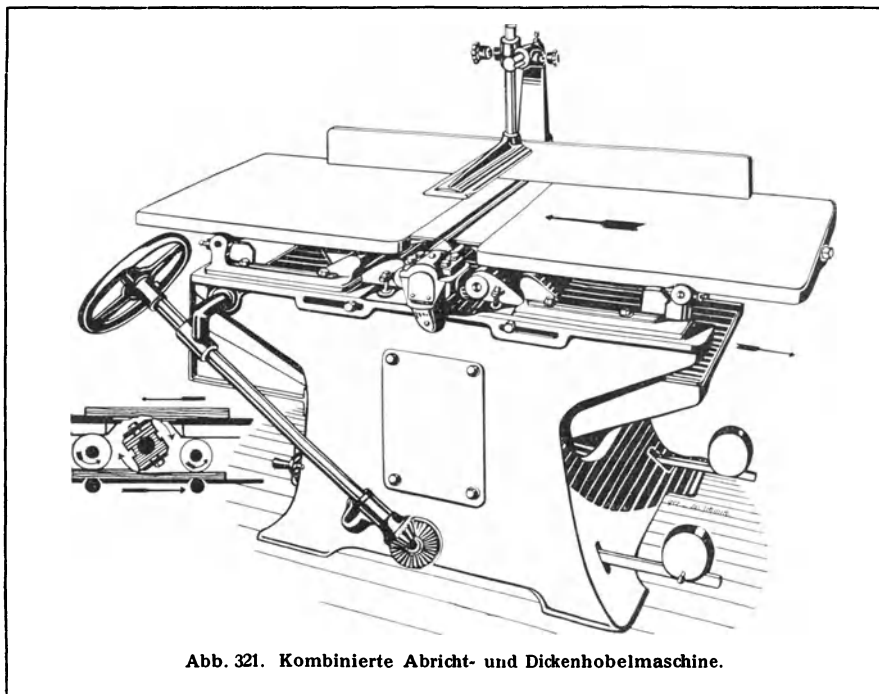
Kombinierte Abricht- und Dickenhobelmaschine.
